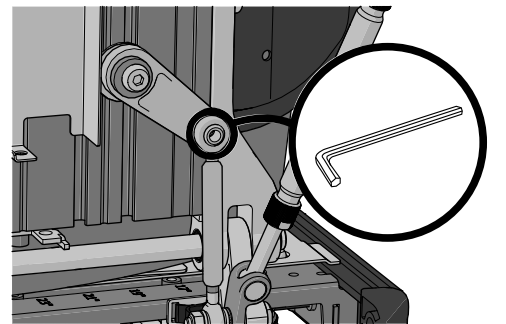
Das Gelenk für die Schiebefunktion der Rückenlehne ist mit einer Schraube befestigt.
